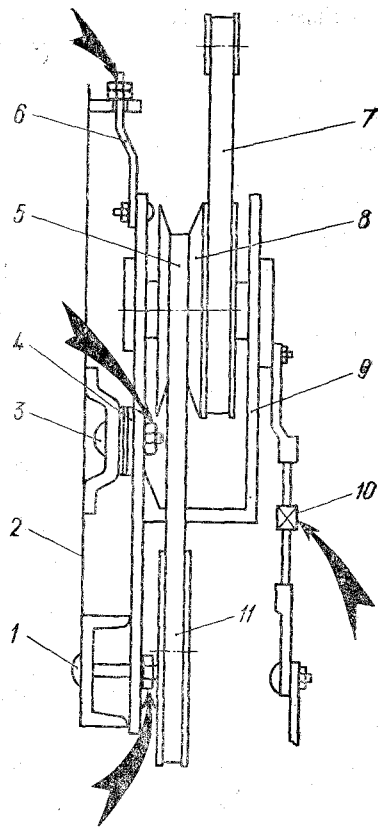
Точки регулювання одноконтурного варіатора механічного привода моста ведучих коліс комбайна «Дон-1500»:
